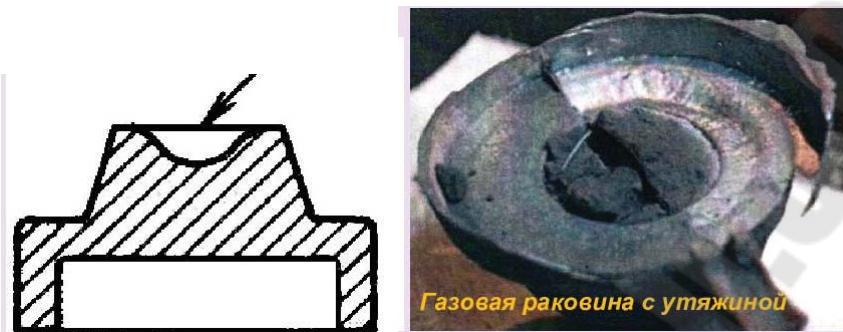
Дефекты отливки: газовая раковина и утяжина
